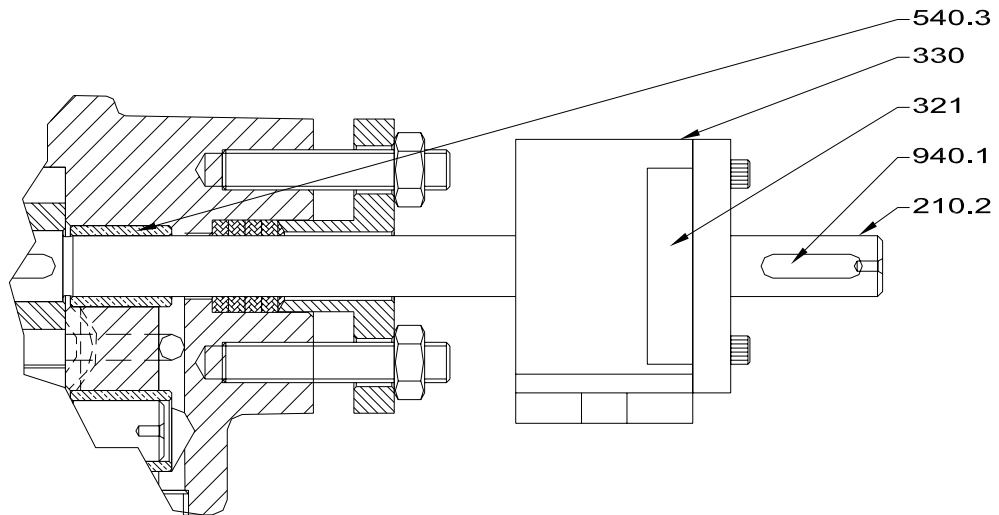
Desenho em Corte bomba FBE c/ Mancal Externo
